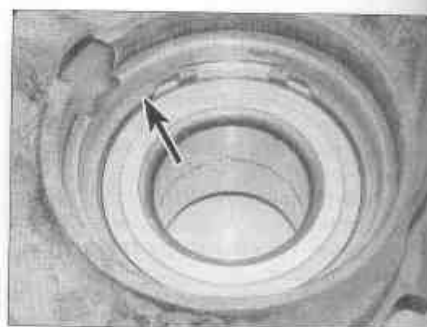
Извлеките стопорное кольцо подшипника (отмечено стрелкой) из поворотного кулака
